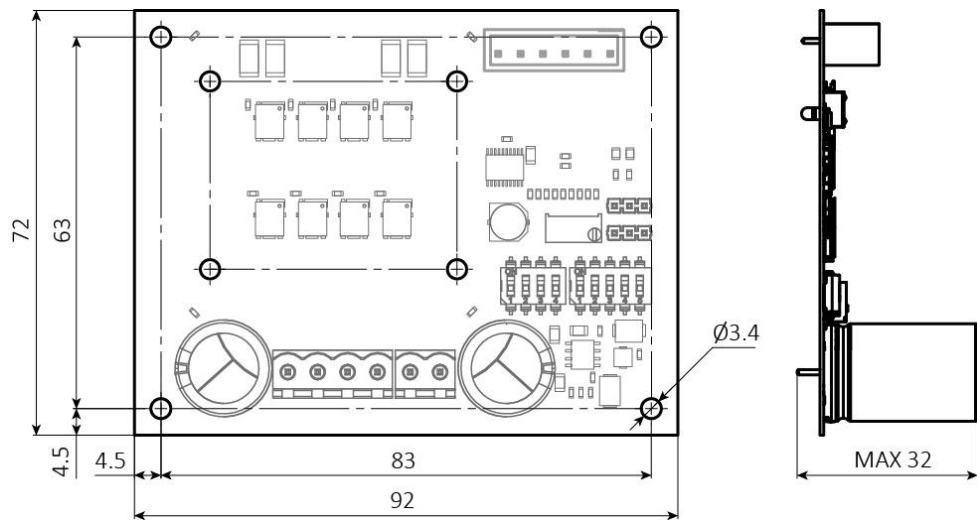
Габаритные и присоединительные размеры драйвера шагового двигателя SMD-4.2.
